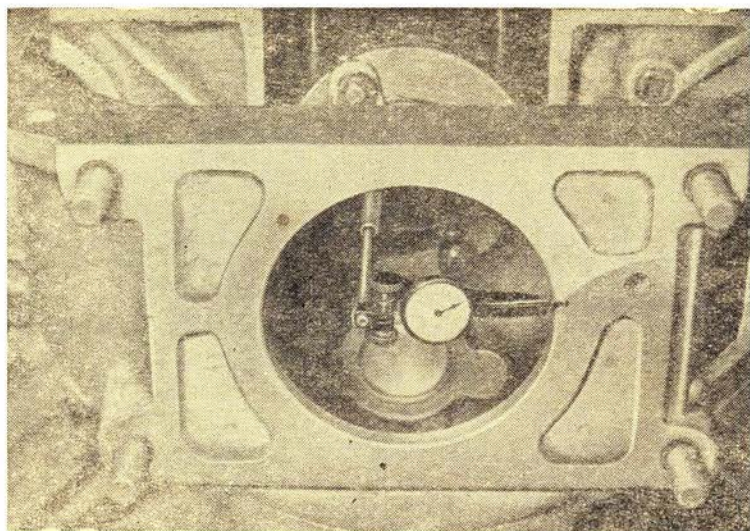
Проверка перпендикулярности торца картера сцепления к оси коленчатого вала
